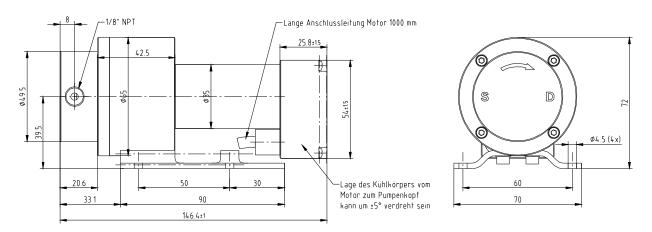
Abmessungen Mikrozahnringpumpe mzr-7255 mit seitlichen Fluidanschlüssen 1/8" NPT
